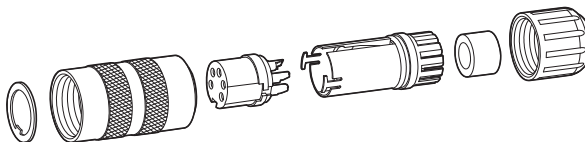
Presa circolare diritta con bloccaggio a vite per cavo a sezione circolare SWD
